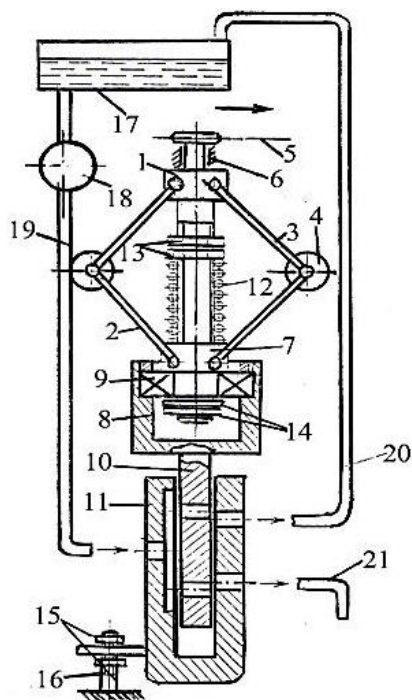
Технологическая схема приспособления для автоматического регулирования рабочей жидкости: 1 — неподвижная плита регулятора; 2, 3 — звено; 4 — груз; 5 — цепная передача; 6 — подстилка; 7 — подвижная плита; 8 — П образная часть; 9 — подшипник; 10 — шибер; 11 — корпус шибера; 12 — пружина; 13, 14 — гайка; 15, 16 — пара винт-гайка; 17 — бак; 18 — насос; 19— 21 — труба
